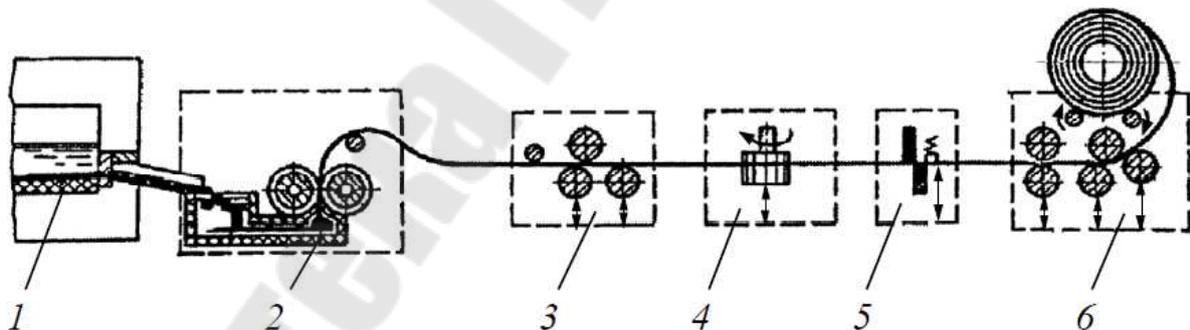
Литейно-прокатный агрегат для производства алюминиевой полосы:
